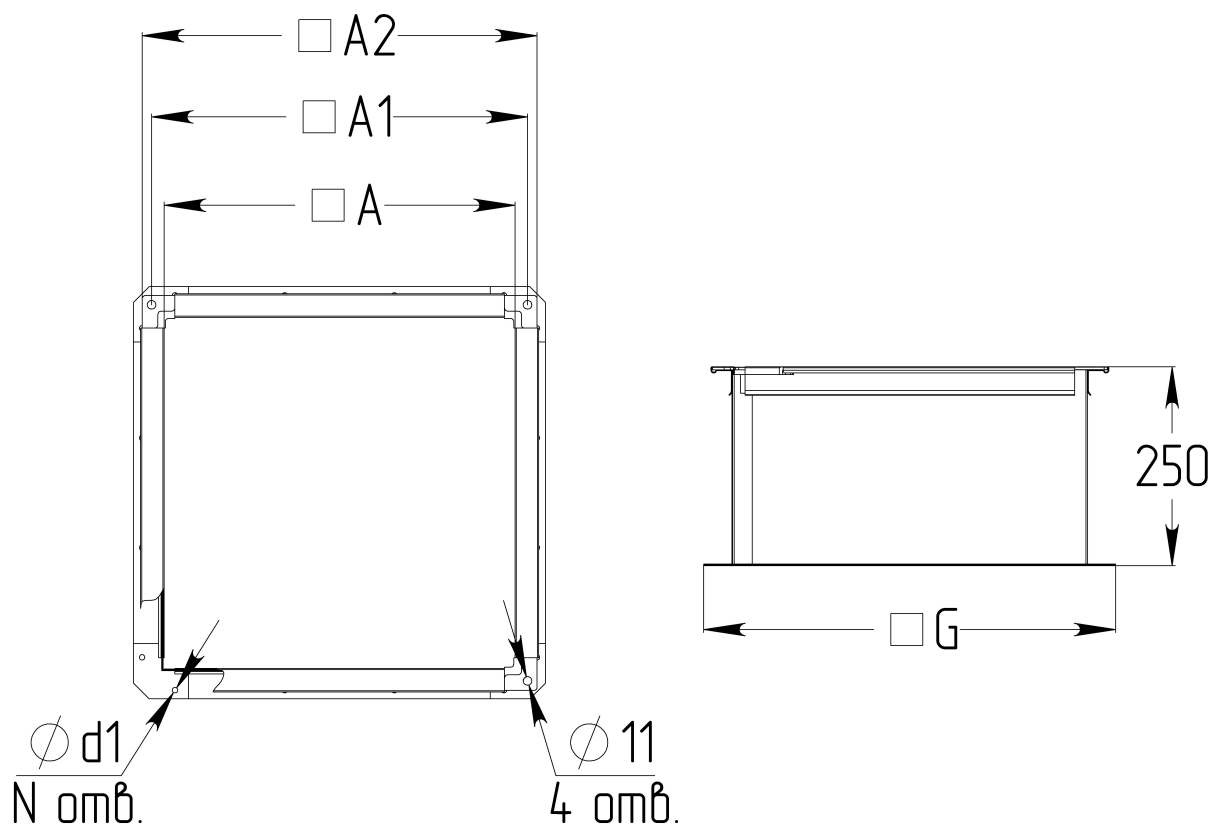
Внешний вид и размеры адаптеров SKV
